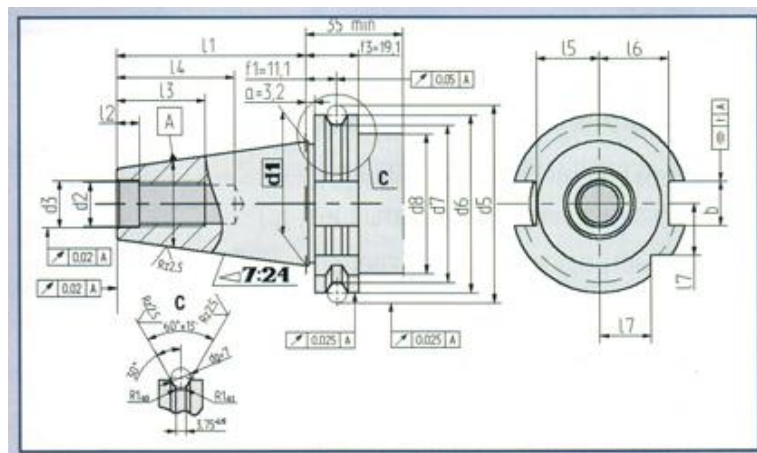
Інструментальний конус Haimer SK50, виконання 2, з внутрішньою подачою ЗОР [9]
